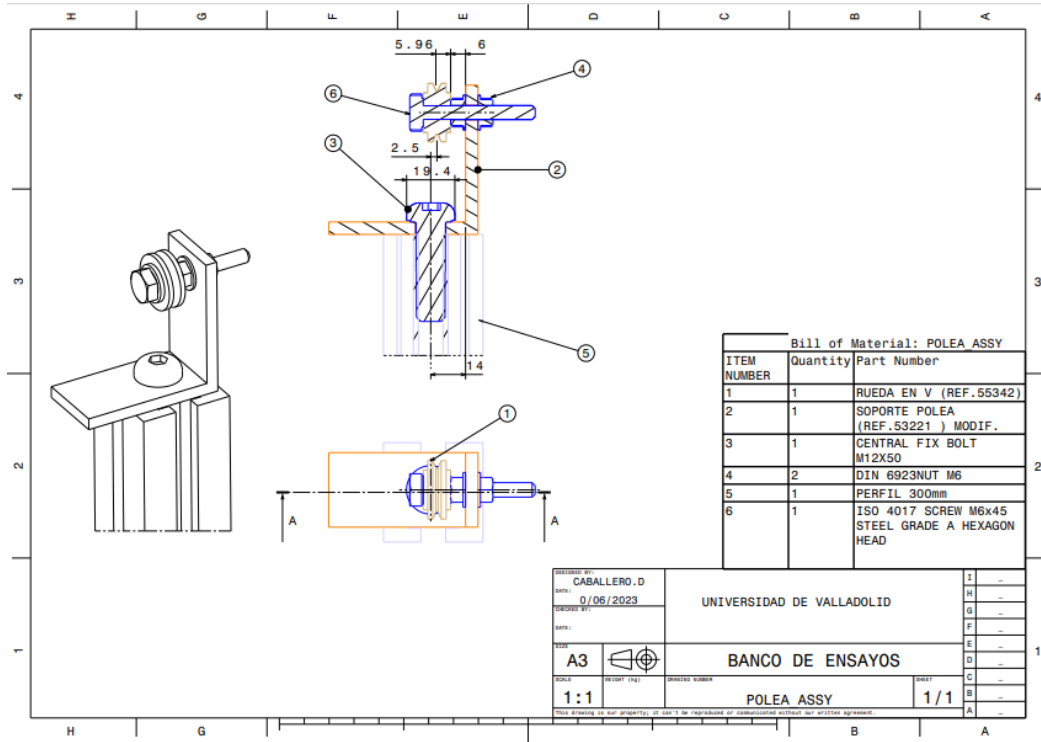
Plano de diseño de ensamblaje (ver completo en ANEXO)
